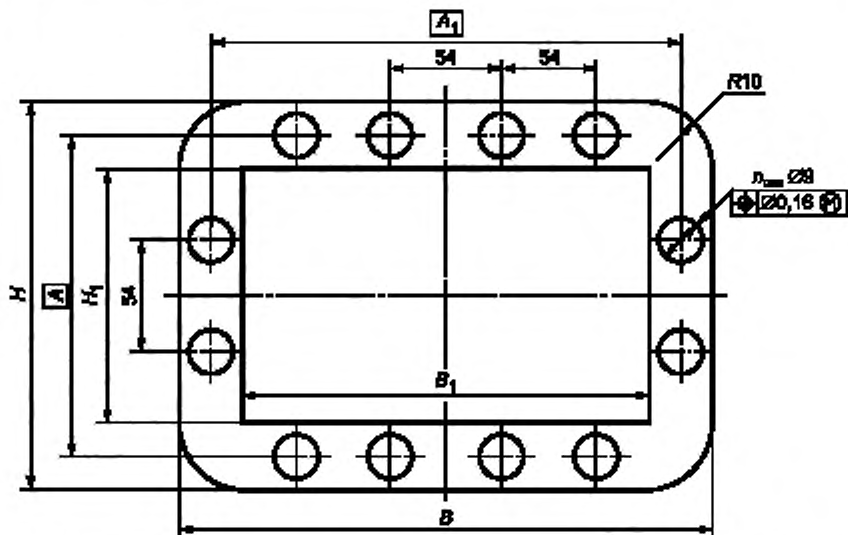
Присоединительные размеры прямоугольных фланцев с расположением четного количества отверстий по сторонам H и B
